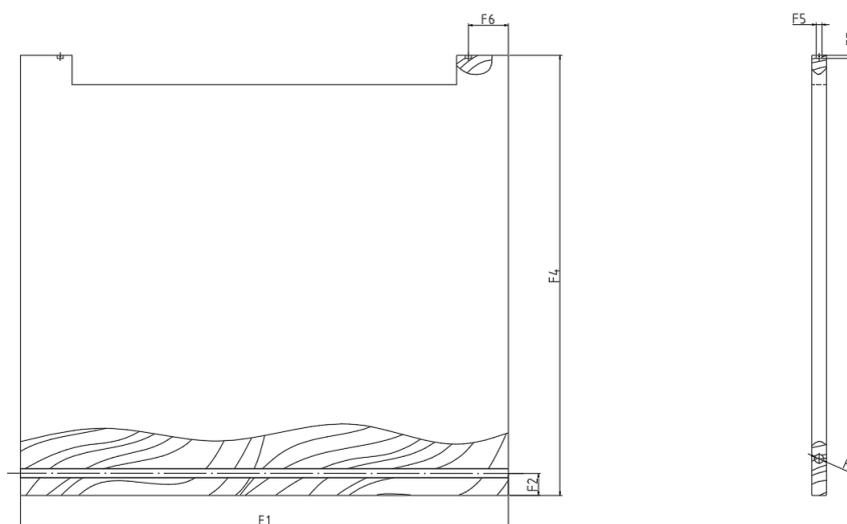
Plano Dimensionado Previo de la Puerta Cajón 2.2.1.1
